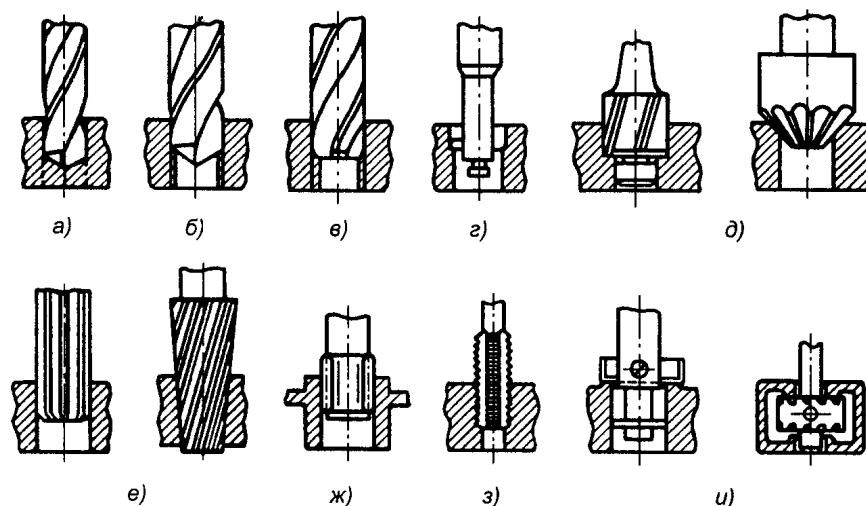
Работы, выполняемые на сверлильных станках: а — сверление отверстий; б — рассверливание; в — зенкерование; г — растачивание; д — зенкование; е — развертывание; ж — выглаживание; з — нарезание внутренней резьбы; и — цекование
